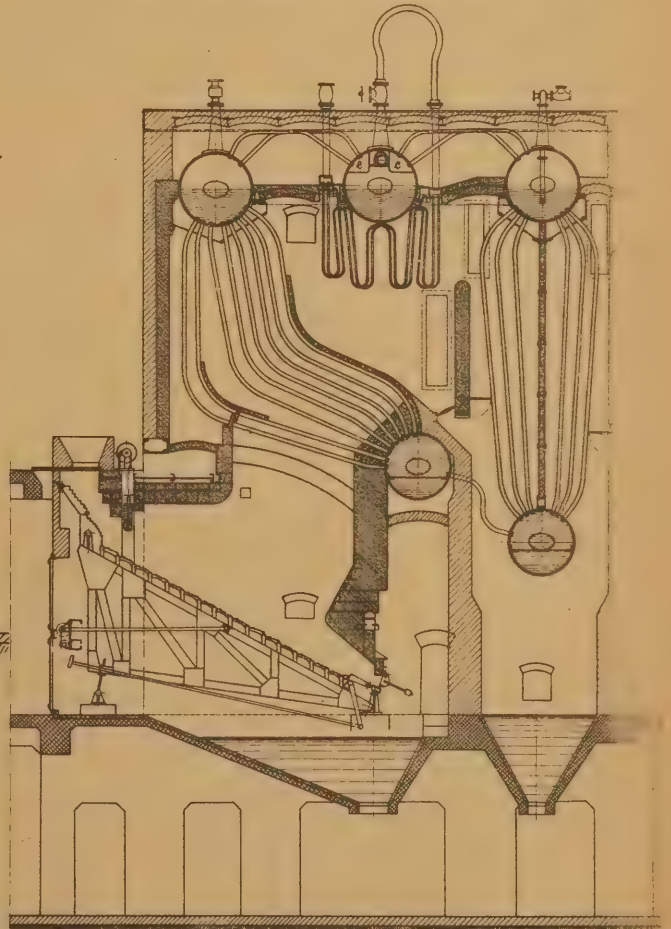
Höchstdruck-Dampfkessel von Gebr. Steinmüller, Gummersbach.
